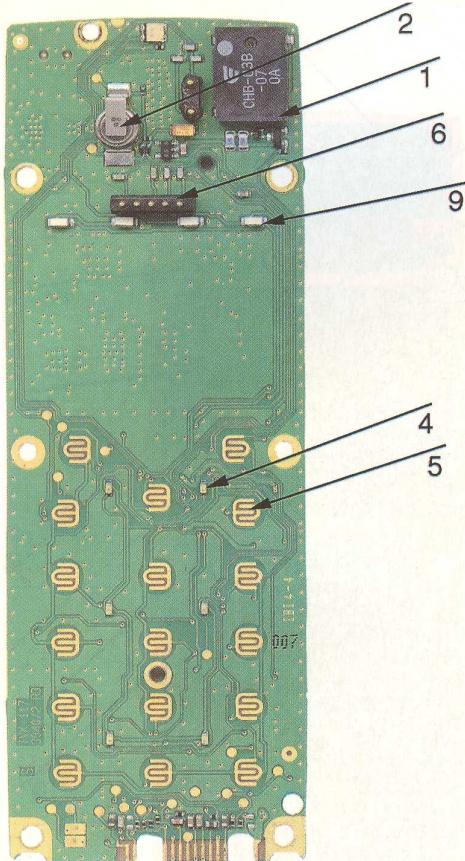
PCB echipat la modelul A1018, față 2 (cu display)
